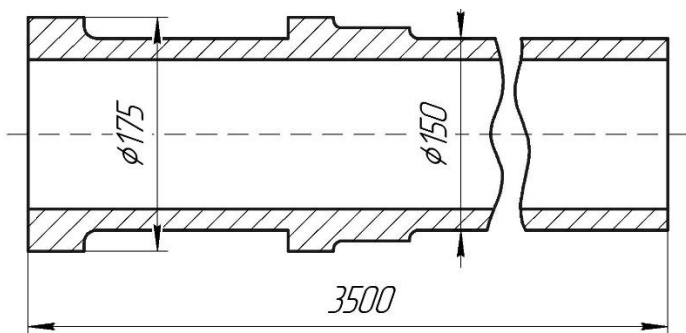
Конструкция из цилиндра, изготавливаемого из поковки
